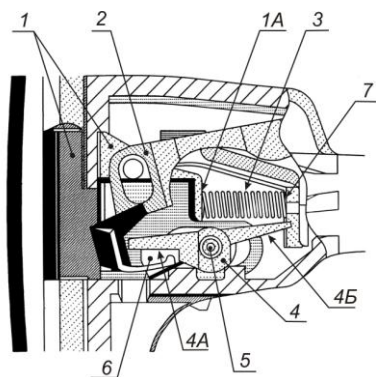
Механизм сцепления автосцепки СА-4:
